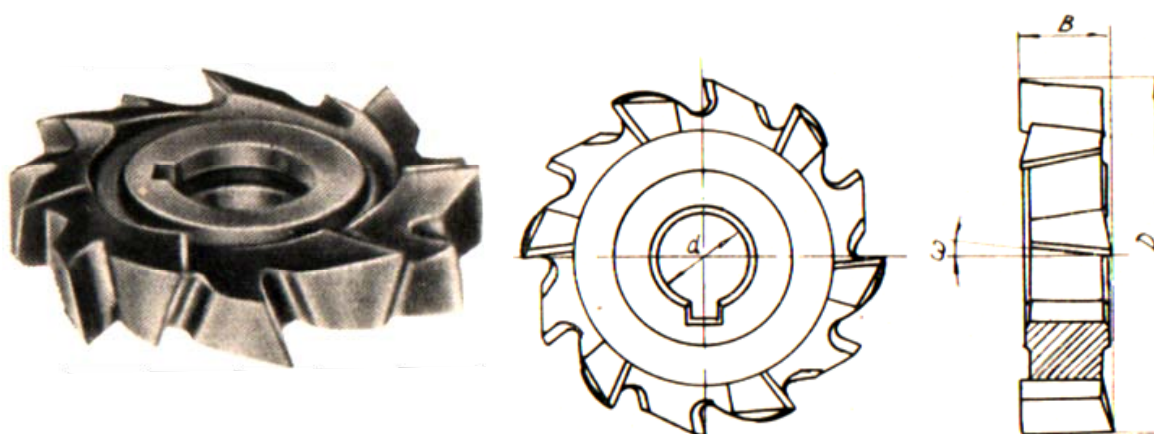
Современная конструкция цельной дисковой фрезы с трехсторонней схемой резания
